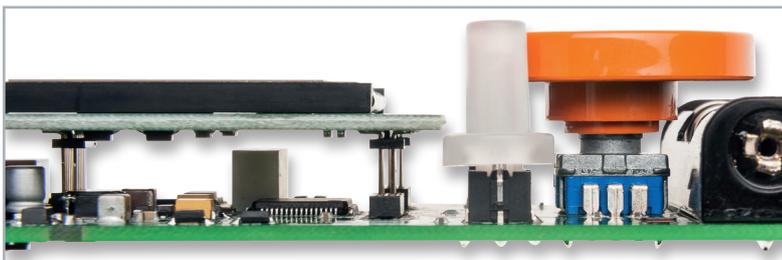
Seitenansicht der fertig aufgebauten Platine mit aufgesetzter Displayplatine
